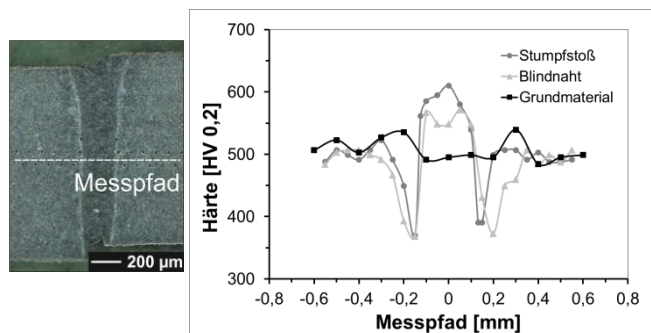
Querschliffaufnahme einer Stumpfstoßschweißnaht (links) und dazugehöriger Härteverlauf (rechts); Parameter: $P_{cw} = 1840 \text{ W}$; $v = 16 \text{ m/min}$; $d_{86} = 53 \mu\text{m}$
